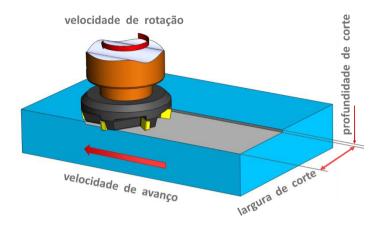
Parâmetros de corte de uma operação de fresagem
